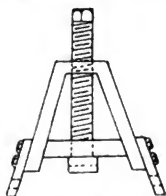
Bewegliche Rahmen mit Schlitten für Handbetrieb.
